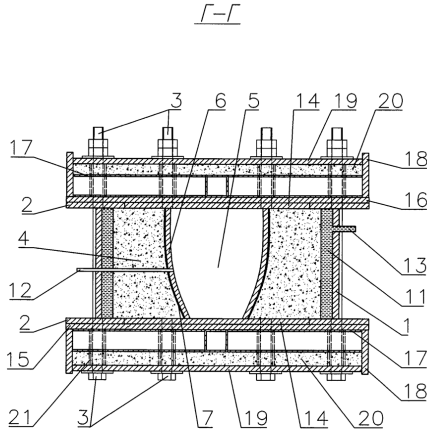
Взрывная камера, вид Г-Г [6], где: 1 – металлический наружный корпус в форме цилиндра; 2 и 3 – верхние и нижние упорные кольца; 4 – силовой элемент; 5 – рабочая полость; 6 – вставка; 7 – компенсационная прокладка; 11 – гидравлическая камера; 12 – вакуумная трубка; 13 – штуцер; 14 – верхний и нижний технологические диски; 15 – дно; 16- крышка; 17 – рёбра жёсткости прямоугольного или профильного сечения; 18 – металлические кольца; 19 – прессующий диск; 20 – фибробетон; 21 – втулки.
